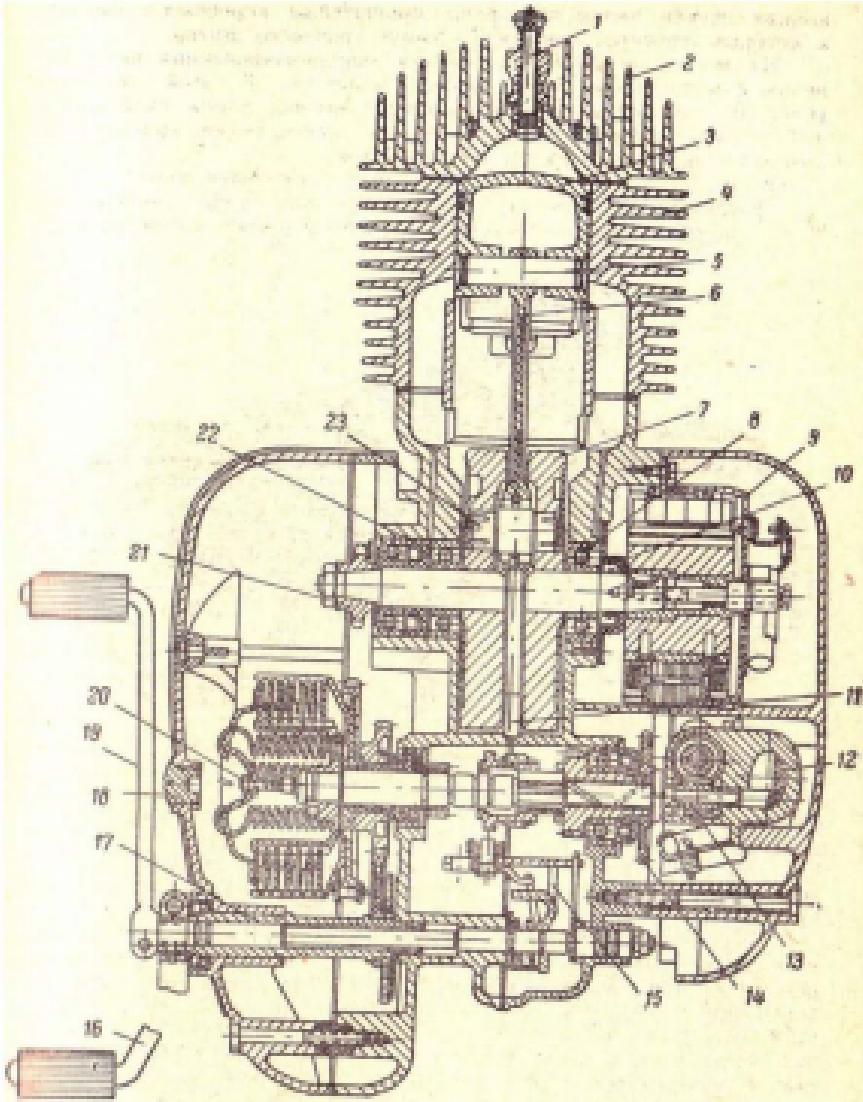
Блок двигателя с коробкой передач мотоцикла К-58:
